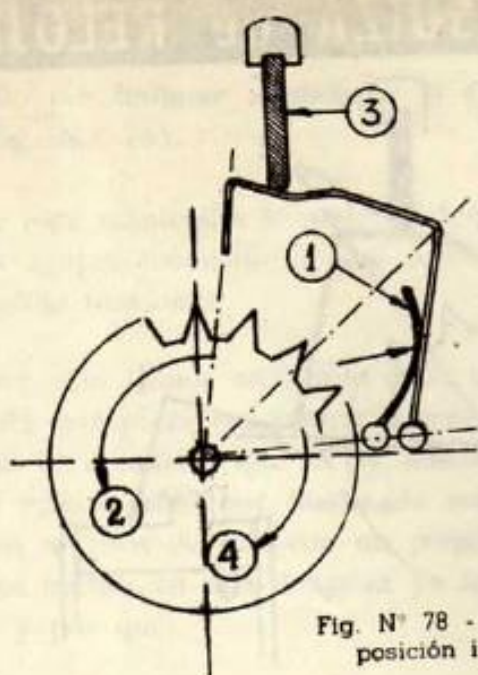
El freno es vuelto a su posición inicial por el resorte 1.
